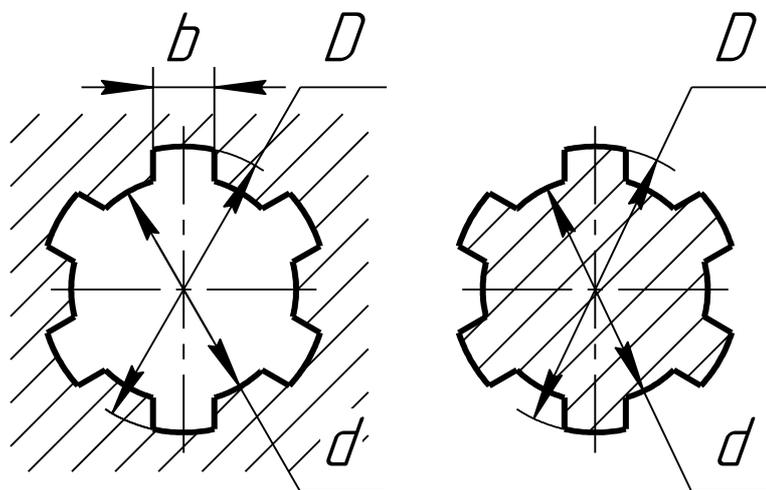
Изображение формы и размеров шлицев в отверстиях и на валу
